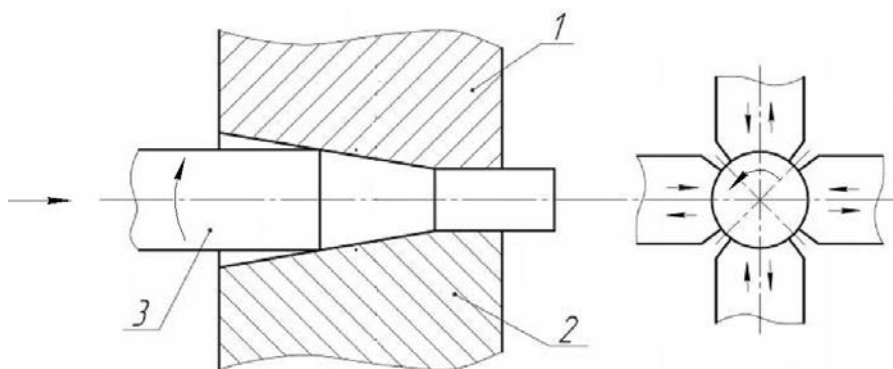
Схема процесса радиального обжатия [3]: 1, 2 – бойки; 3 – заготовка
